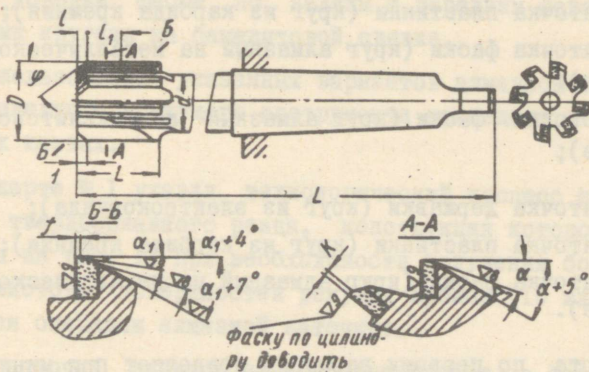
Углы заточки твердосплавной развертки под алмазную обработку.
